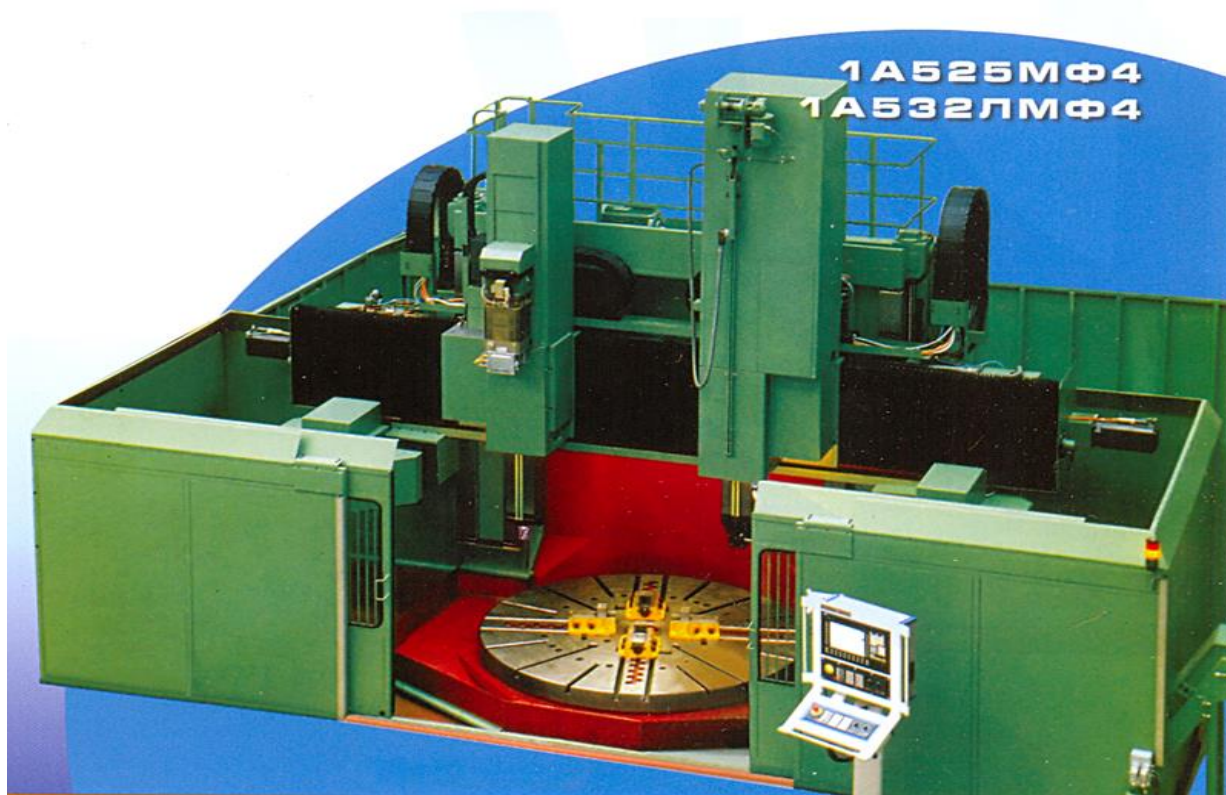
Станок токарно-карусельный многоцелевой 1А525МФ4
